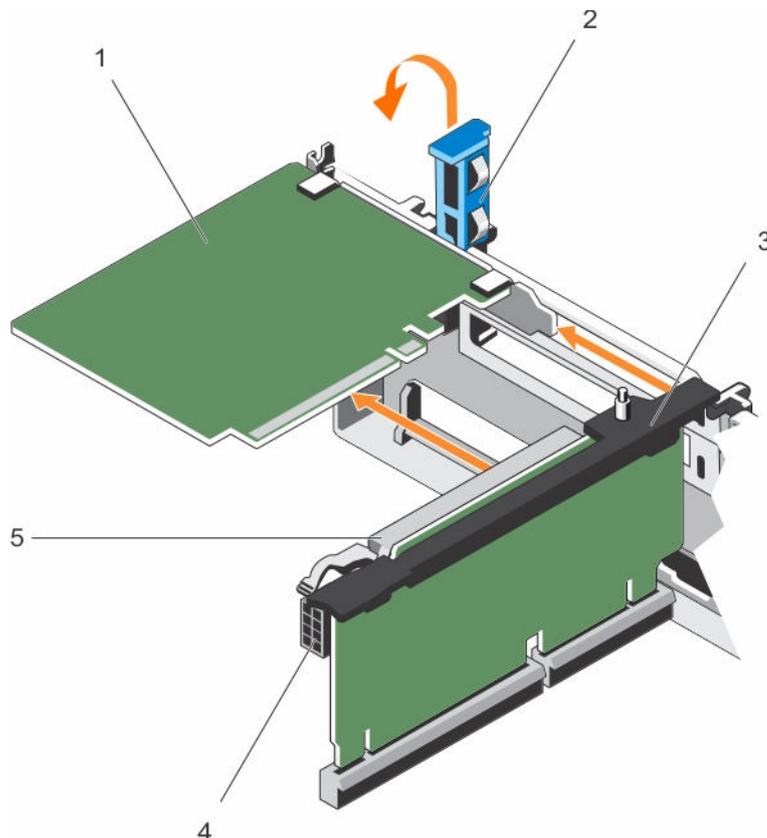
Remover uma placa de expansão da riser de placa de expansão 2 ou 3
